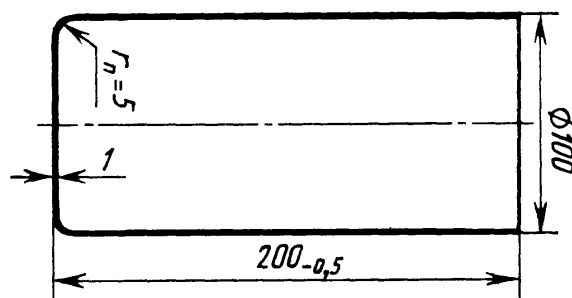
Чертеж детали, получаемой вытяжкой
